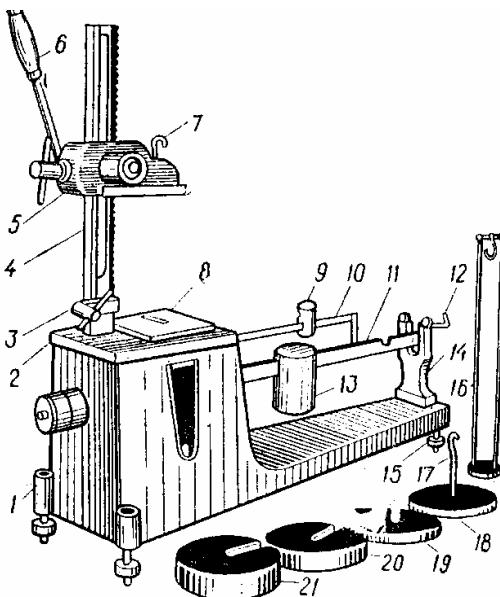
Пристрій для перевірки довжини пружин і пружності пружин та поршневих кілець:
